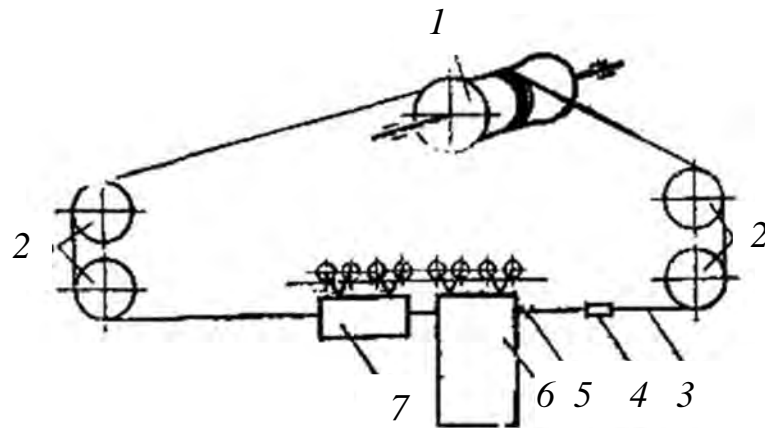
Схема механизма передвижения тележки при расположении привода на мосту: 1 – барабан; 2 – отклоняющие блоки; 3 – канат; 4 – регулирующее устройство; 5 – пружинный амортизатор; 6 – кабина управления; 7 – тележка
